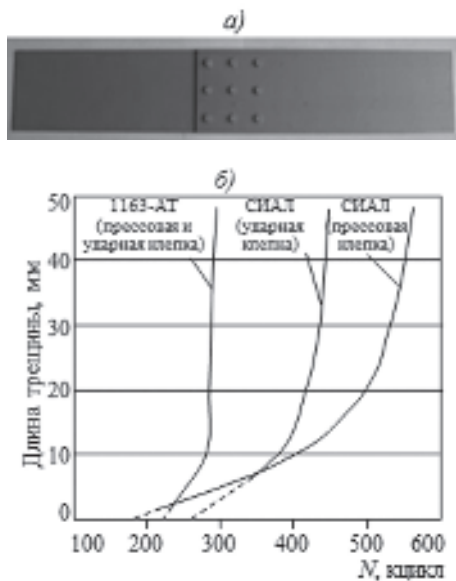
Вид образца трехрядного заклепочного соединения внахлест (а) и кривые развития трещин усталости в заклепочных соединениях (б)
